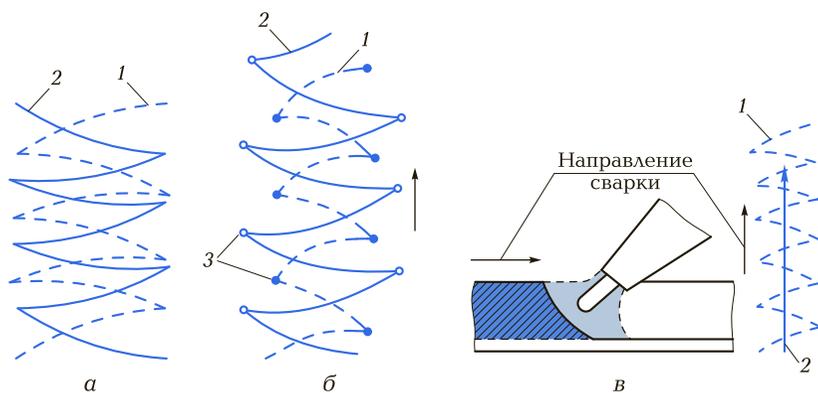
Движения горелки и проволоки при сварке:
